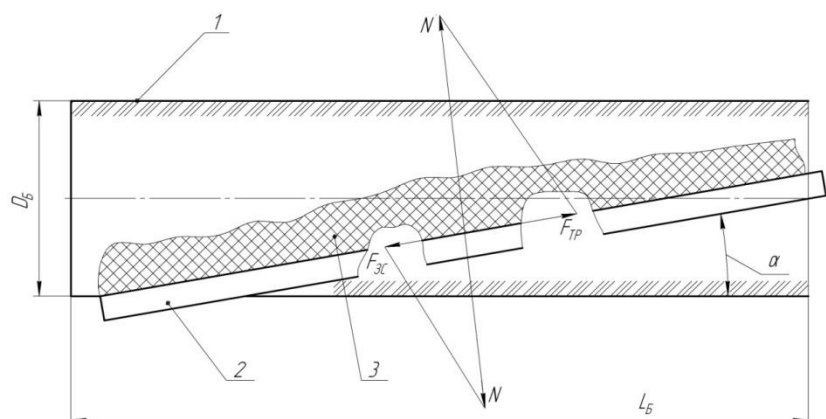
Розрахункова схема до визначення кута постановки планки до осі обертання барабану: 1- барабан; 2 – планка 3 – шар ґрунту
